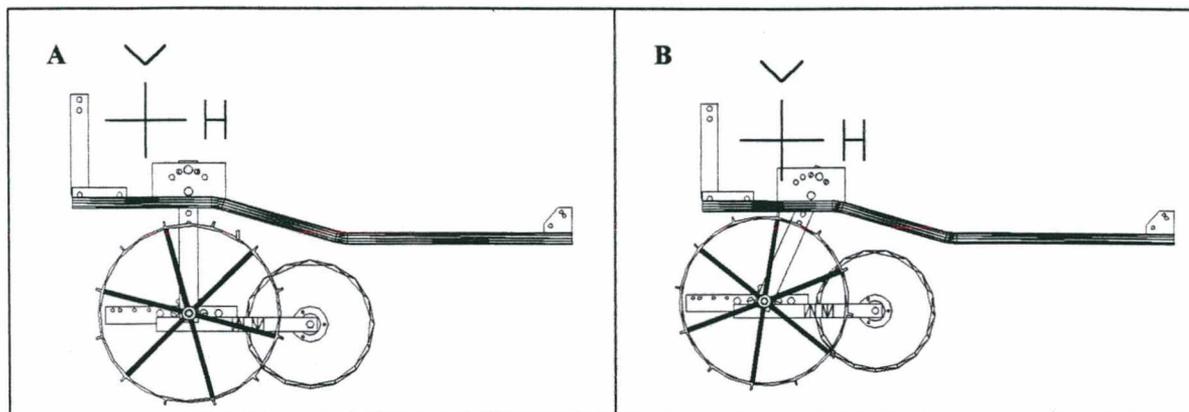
A) Rodas com suporte na horizontal; B) Rodas com suporte para frente.
